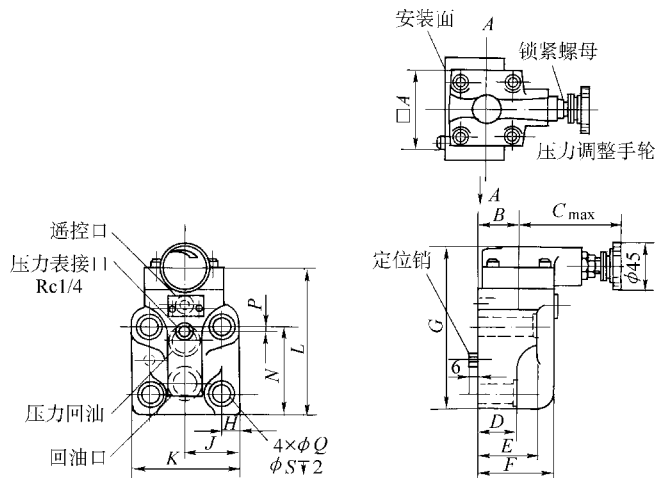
BG 型先导式溢流阀外形尺寸图
